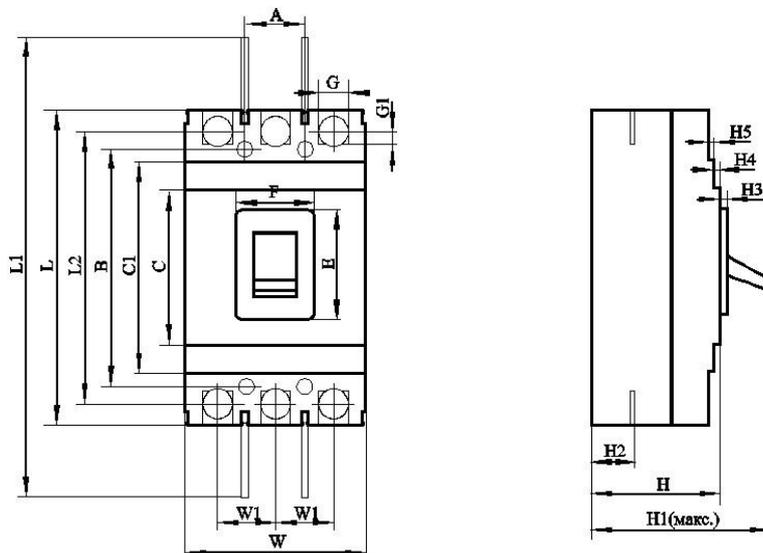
Габаритные и установочные размеры выключателей ВА77-400, ВА77-630, ВА77-800, ВА77-1250.
